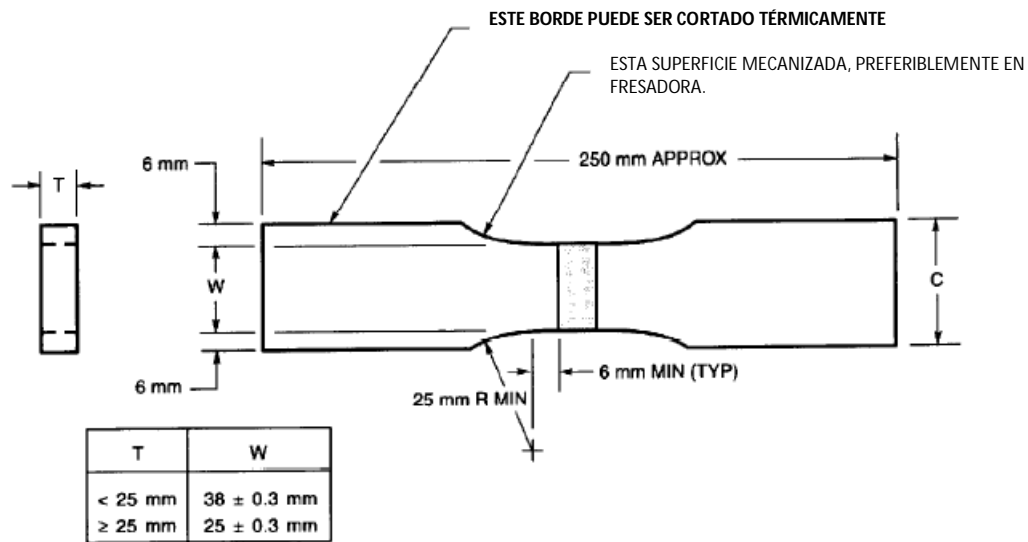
Probeta resistencia a la tensión junta soldada. Figura A.12. (AWS, Standard Methods for Mechanical Testing of Welds, 2010)
